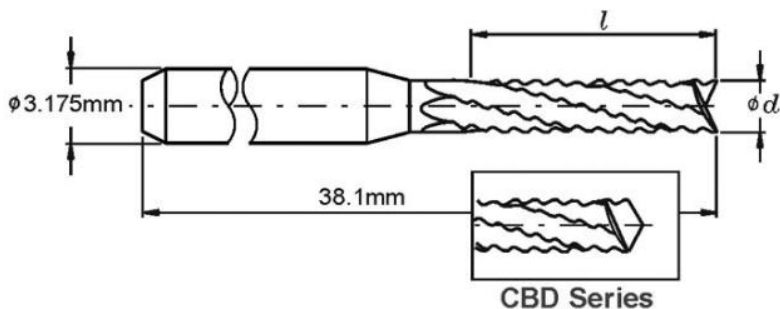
Концевые фрезы типа CBF и CBD [11]
